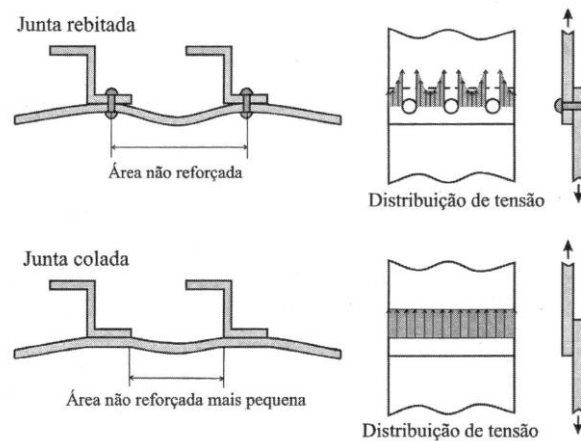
Distribuição da tensão em juntas rebetadas e coladas [3].
